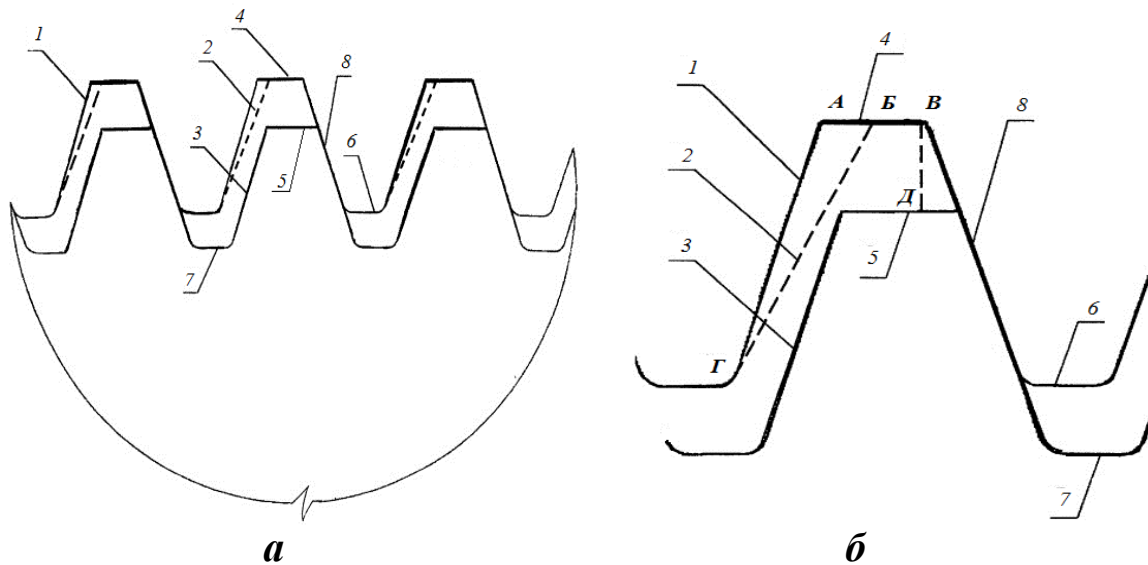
Відновлення профілю зношеної зубчасті частини крупногабаритної шестерні:
